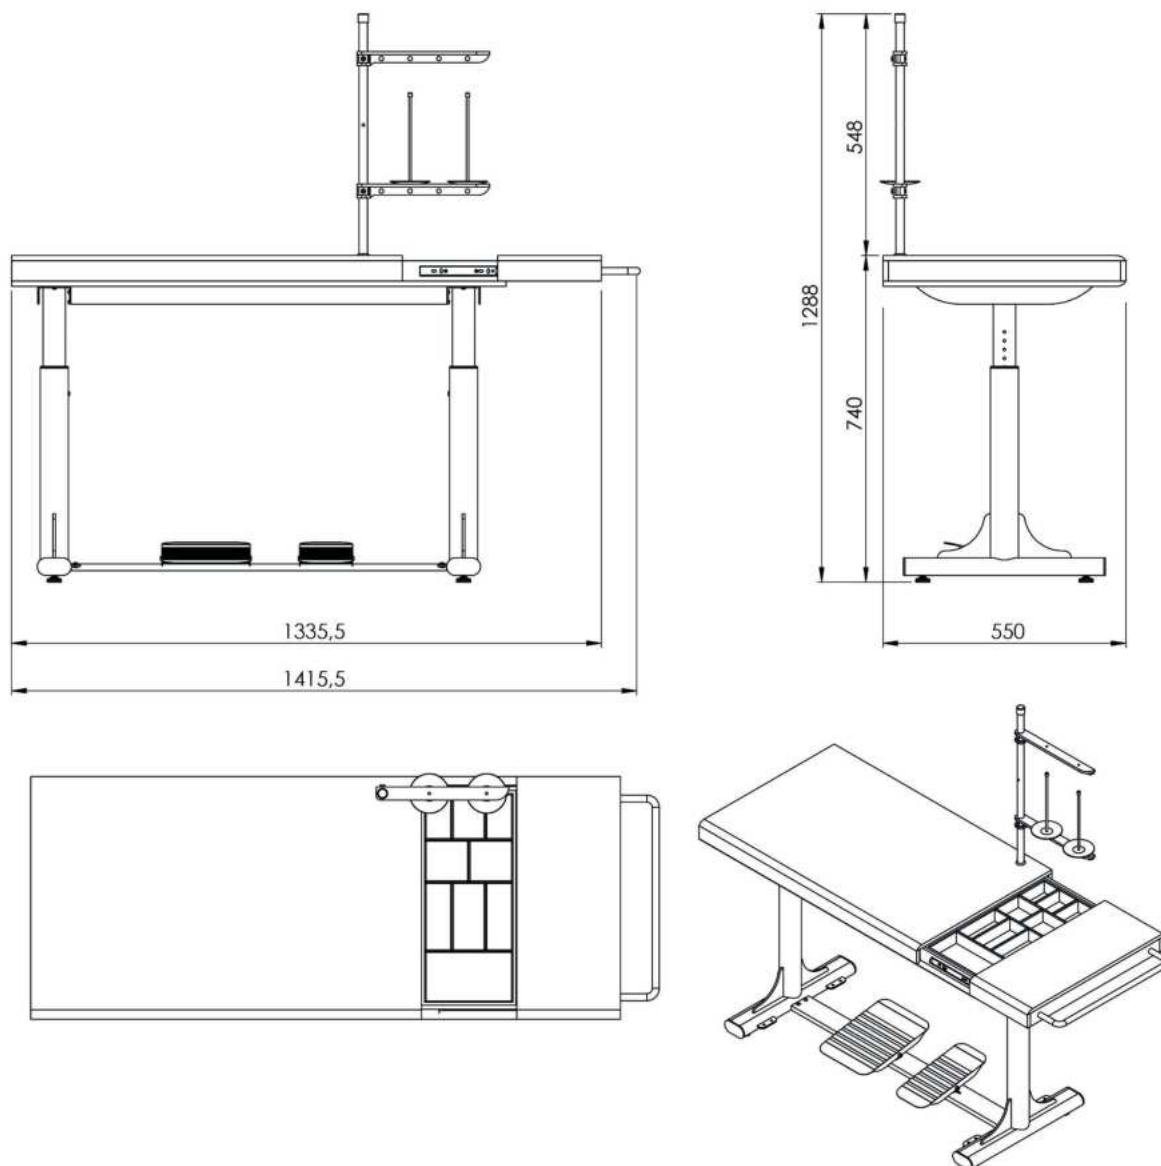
Dimensões gerais - Mesa Montada e Aberta
